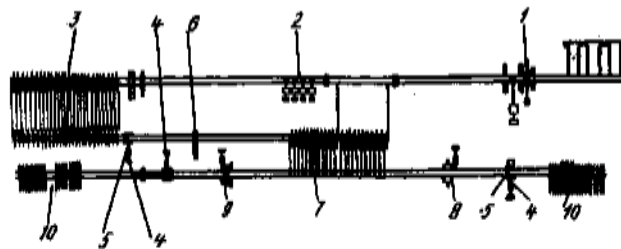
Схема расположения оборудования толстолистового стана с непрерывной чистовой группой:
